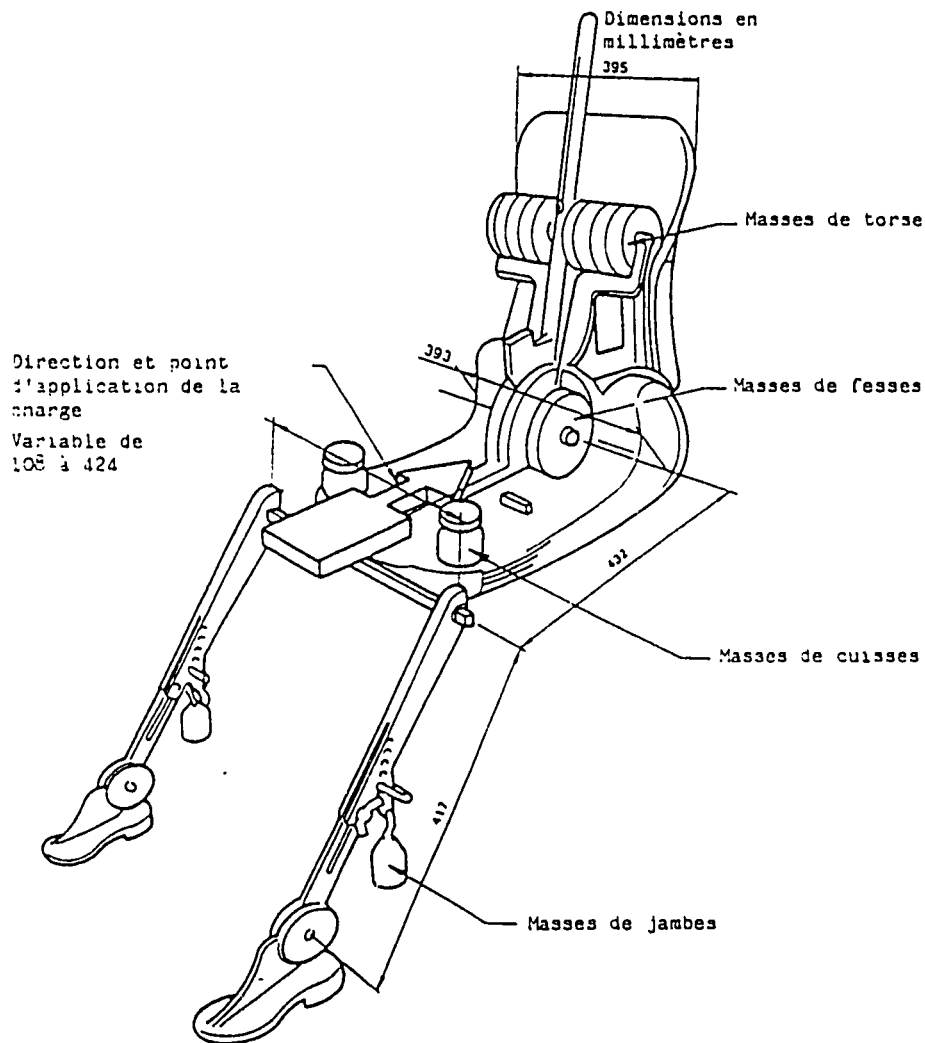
Dimensions des éléments de la machine 3-D H et emplacement des masses
